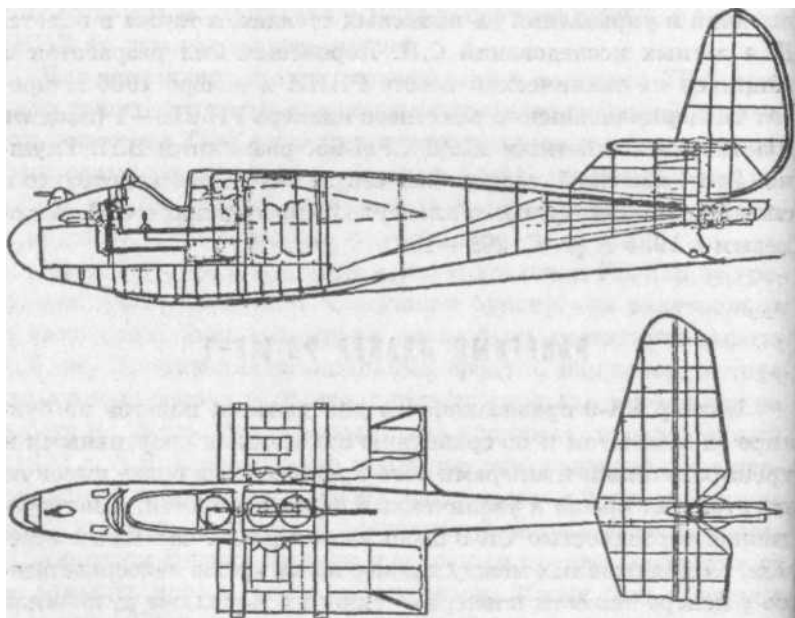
Компоновочная схема ракетного планера РП-318—1
